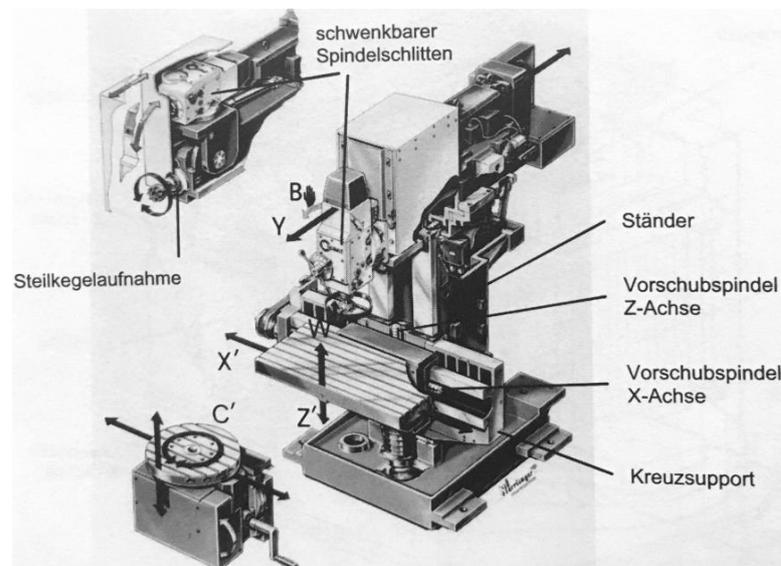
Universalfräsmaschine (vertikale Werkzeugspindel)
